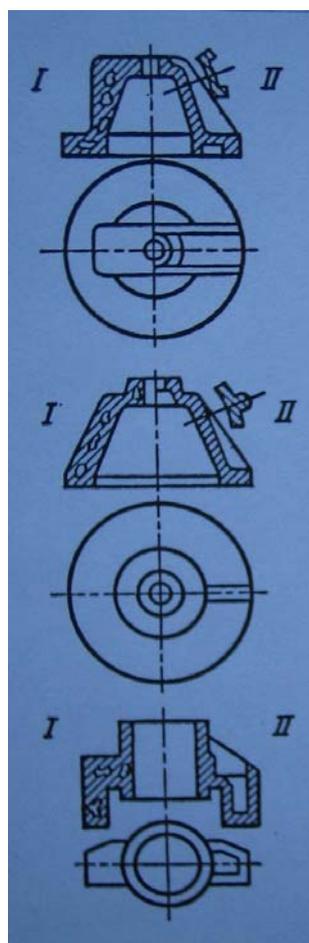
Полости в отливках, полученных литьем под давлением: а – конструкция отливки, позволяющая использовать постоянные стержни; б –
